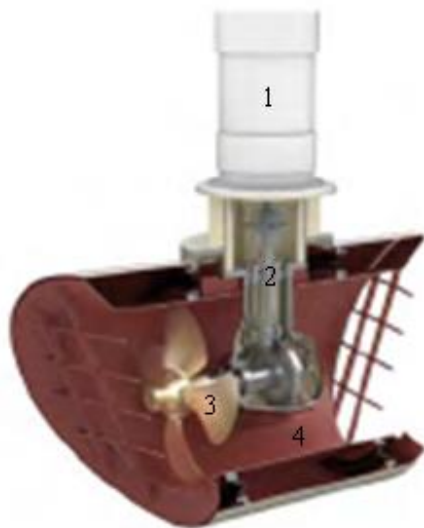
Подруливающее устройство: 1 – двигатель; 2 – редуктор; 3 – винт; 4 – труба
